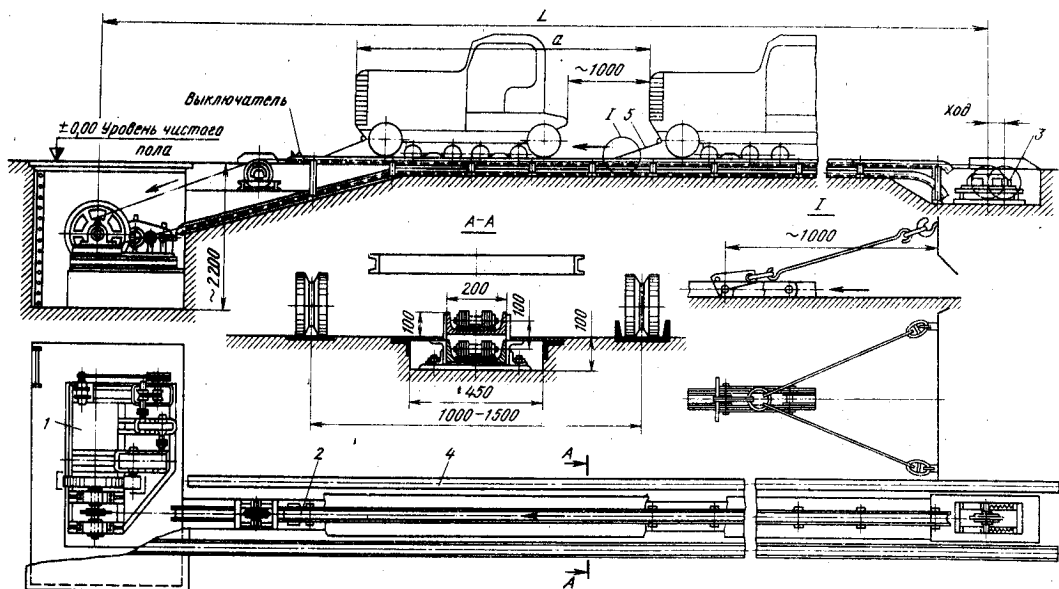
Вертикально замкнутый цепной конвейер для сборки тракторов: 1 — привод; 2 — тяговая цепь; 3 — натяжное устройство; 4 — направляющий путь; 5 — сценка
